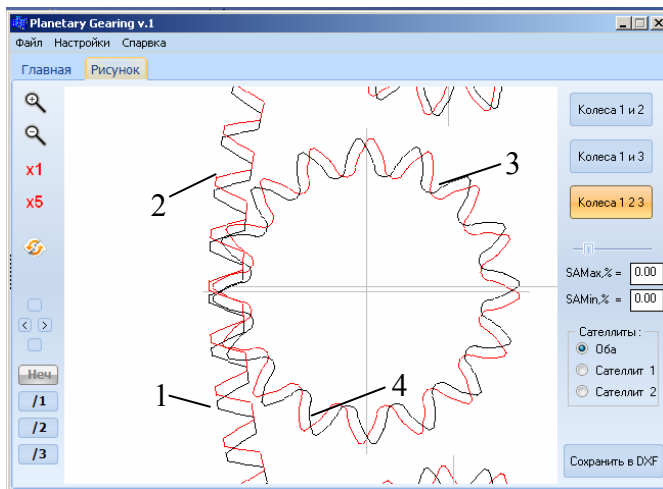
Фрагмент зацепления двухвенцового промежуточного сателлита с опорным и подвижным зубчатыми колесами с внутренними зубьями: 1 – опорное зубчатое колесо  $z_3=100$ ; 2 – подвижное зубчатое колесо  $z_2=99$ ; 3 – зубчатый венец сателлита  $z_1=16$  в зацеплении с колесом  $z_3$ ; 4 – зубчатый венец сателлита  $z_1=16$  в зацеплении с колесом  $z_2$
